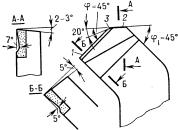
Резец с зачищающей режущей кромкой: 1 — главная режущая кромка; 2 — переходная режущая кромка; 3 — зачищающая кромка.
